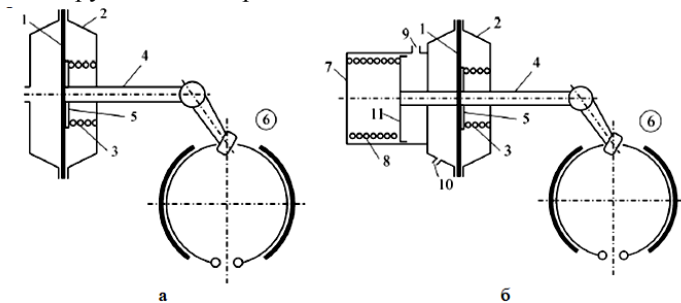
Схемы тормозных камер: а – диафрагменная; б – с пружинным энергоаккумулятором: 1 – диафрагма; 2 – корпус; 3 – пружина; 4 – шток; 5 – опорный диск; 6 – тормозной механизм; 7 – цилиндр энергокамеры; 8 – энергопружина; 9 – штуцер шланга стояночной системы; 10 – штуцер шланга основной системы; 11 – поршень
